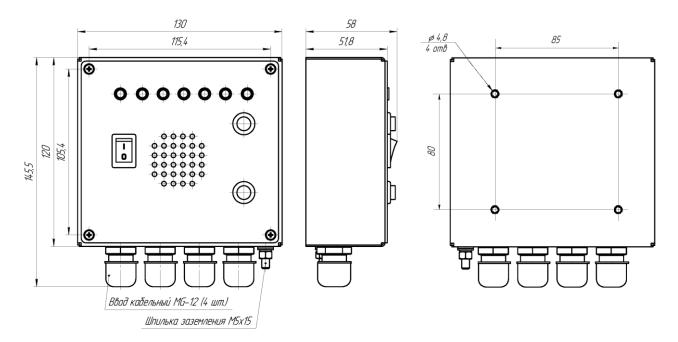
Габаритные и установочные размеры БС-206
